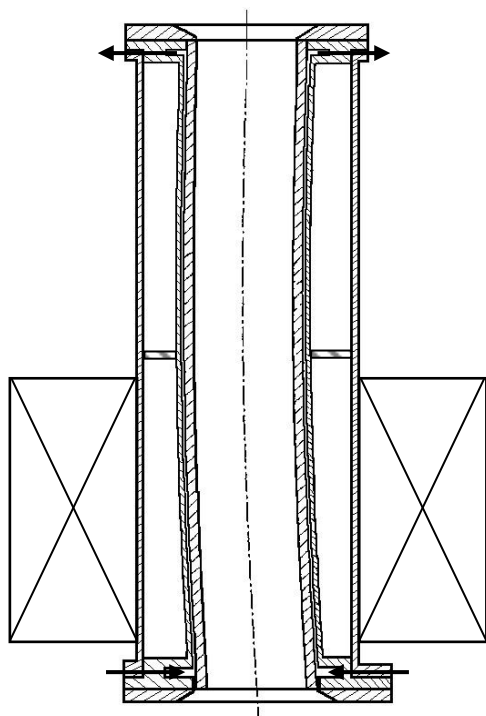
Схема расположения катушки устройства электромагнитного перемешивания металла в нижней части кристаллизатора
